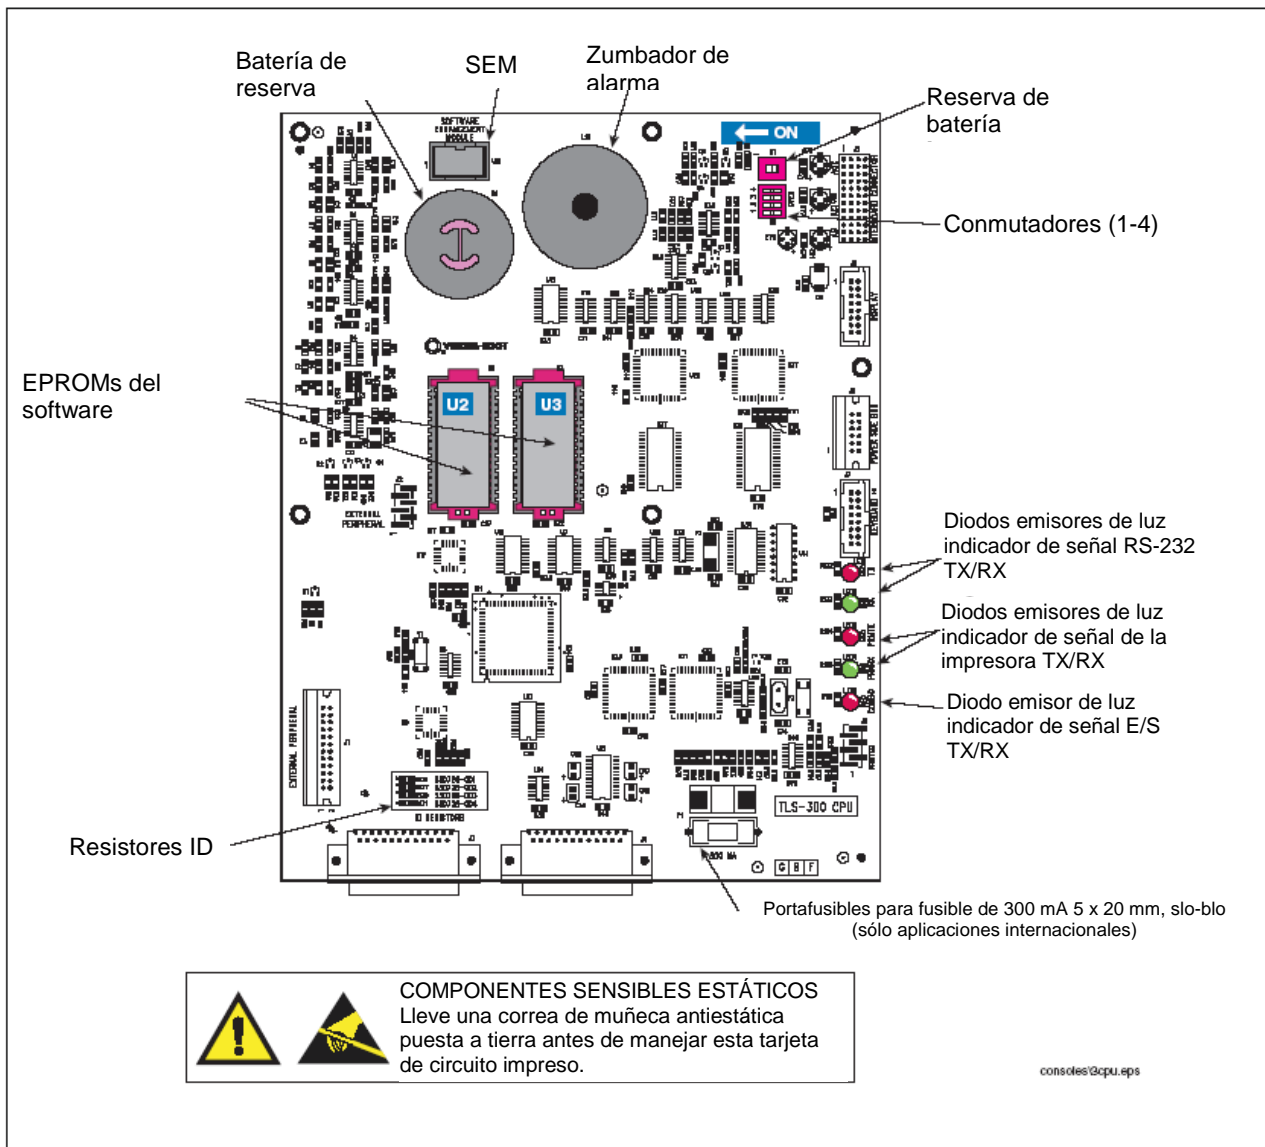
Disposición de la tarjeta CPU de la consola de la Serie TLS-300 con componentes de montaje en superficie
